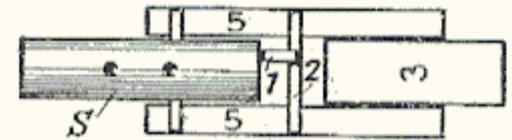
/3. Schnitt durch die Lagerung des Schießblockes S.
